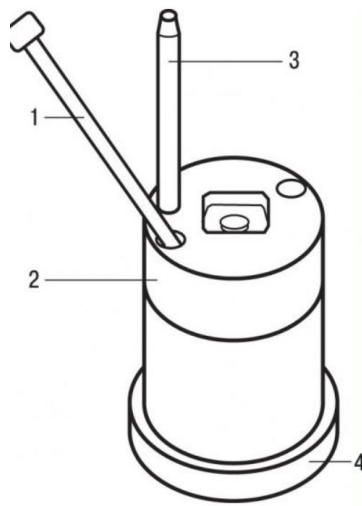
Положення пристроїв на шарнірі опорного кронштейна балки задньої підвіски для запресування: 1 - напрямний елемент/опора 0543-B; 2 – болти 0543-G; 3 - напрямна тяга 0543-F; 4 - упорна пластина шарніра 0543-A
